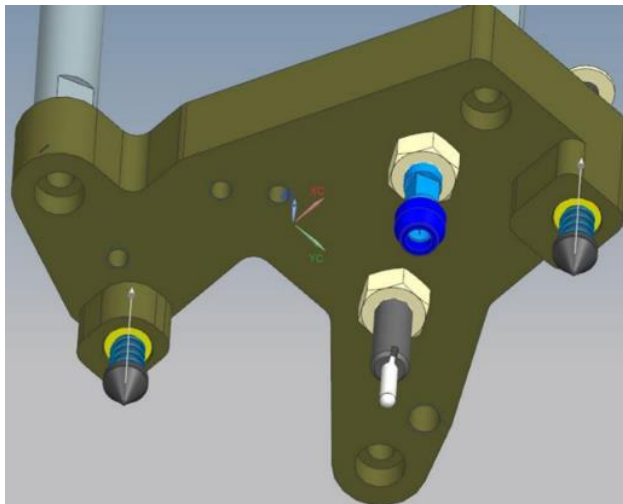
3D CAD-модель центруючого вузла лівої частини центрувальної головки
